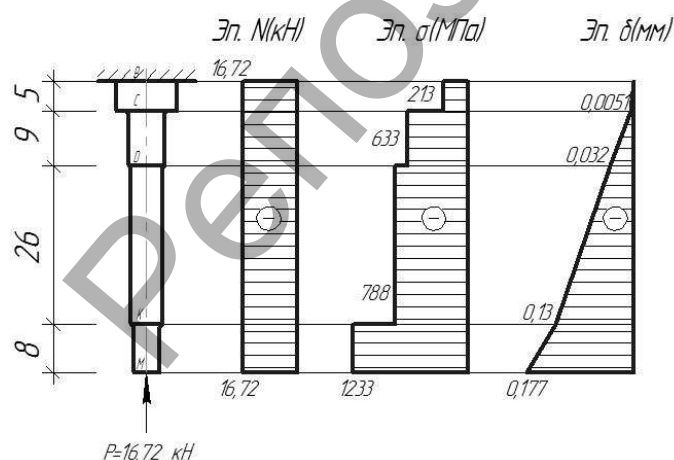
Эпюры продольных сил, нормальных напряжений и перемещений поперечных сечений для экспериментального пуансона
